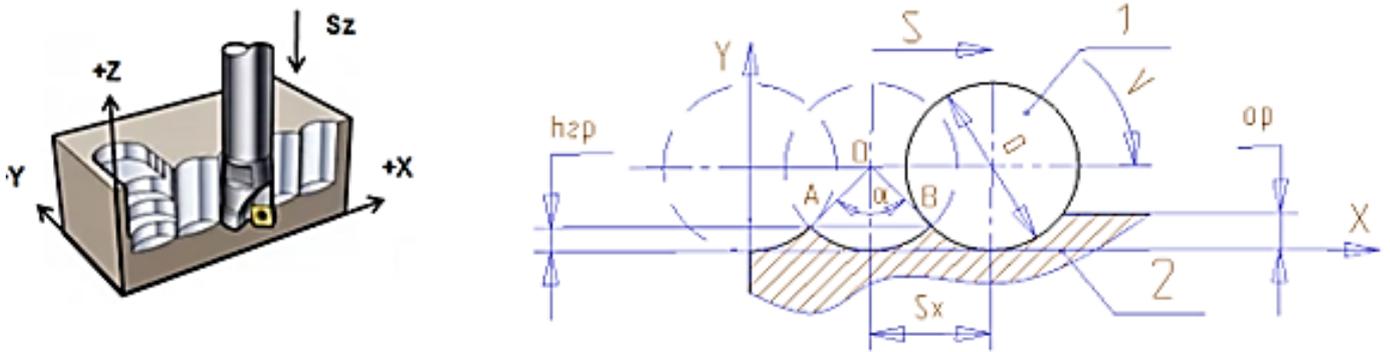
Компьютерная модель формирования неровности при плунжерном фрезеровании: 1 – контур фрезы; 2 – обрабатываемая поверхность;  $V$  – направление вращения фрезы;  $S$  – направление подачи фрезы вдоль обрабатываемой поверхности;  $h_{gr}$  – высота «гребешка»;  $a_p$  – глубина резания;  $S_x$  – величине однократного смещения фрезы вдоль обрабатываемой поверхности;  $l_{gp}=S_x$  – длина основания «гребешка»;  $D$  – диаметр фрезы
